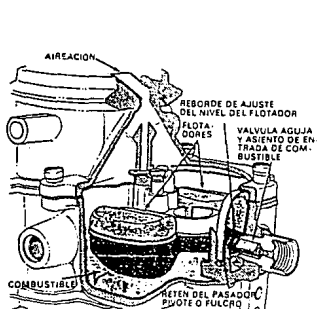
Corte parcial de un carburador mostrando el circuito de flotador.
